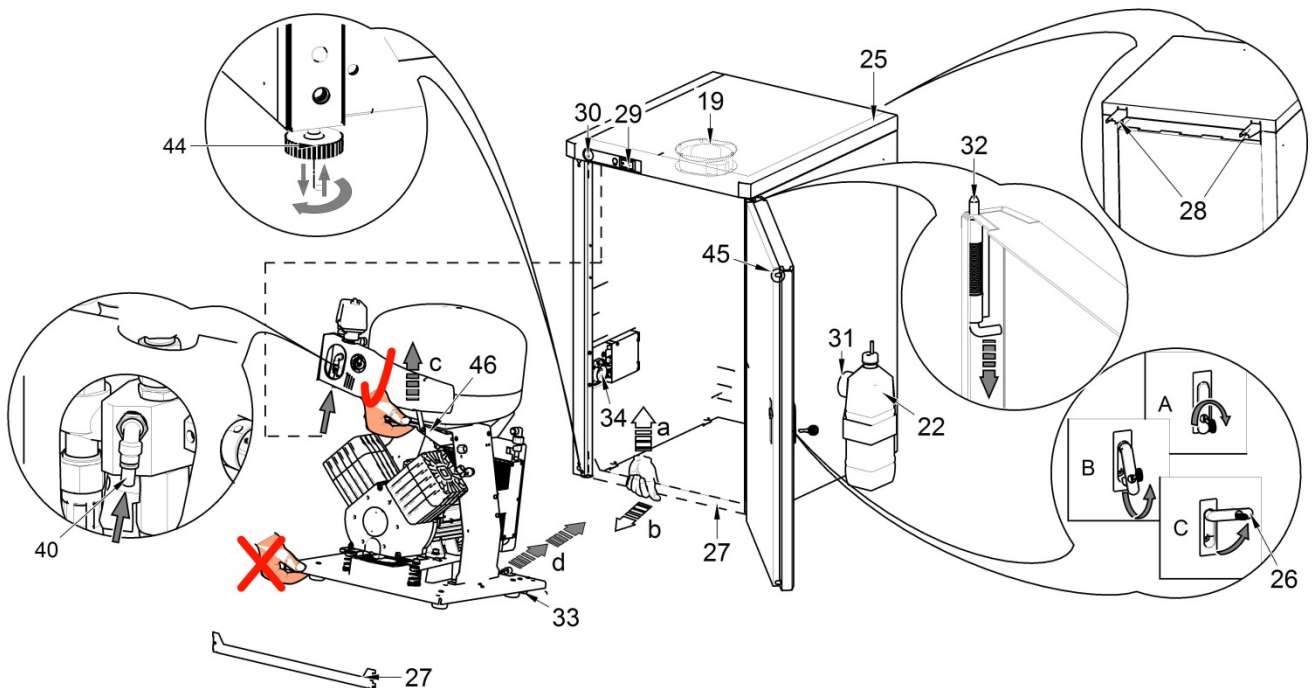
Kompresor s membránovou sušičkou vzduchu
